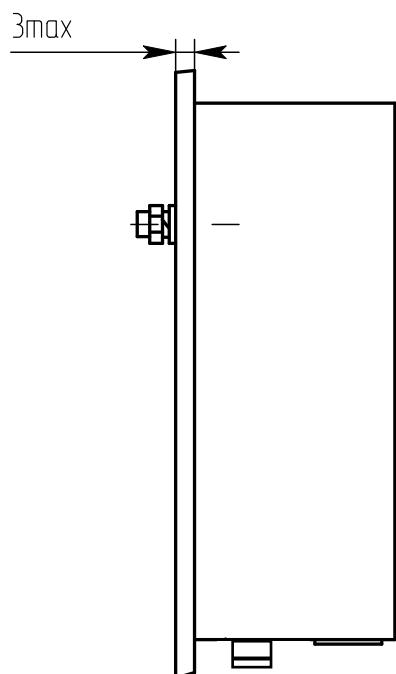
Крепление со стороны боковой стенки кожуха
